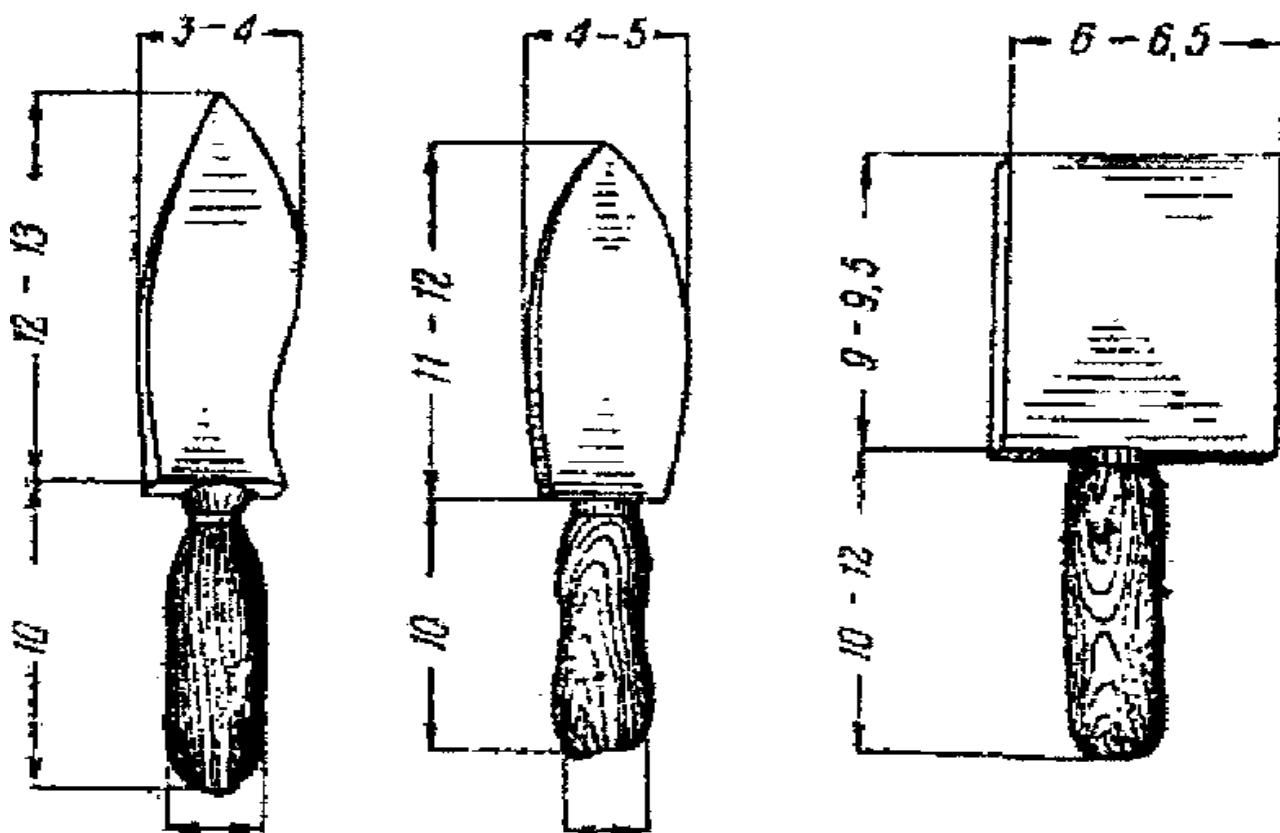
Ножі для оброблення риби (розмір у див): а – лящик; б – камбалка; в – шкерельний.
